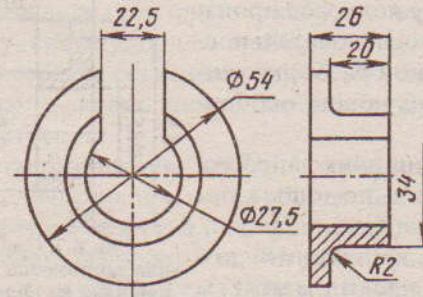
Оправка для выпрессовки подшипника с полуоси
